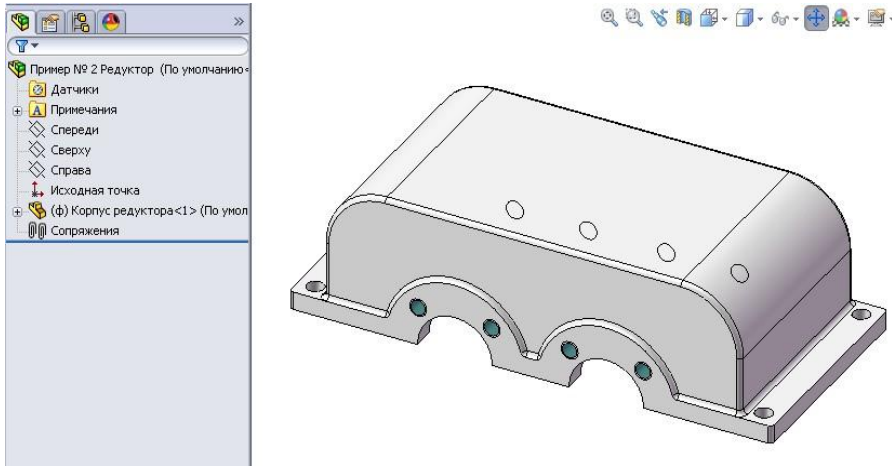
Додана деталь «Корпус редуктора» в складання
